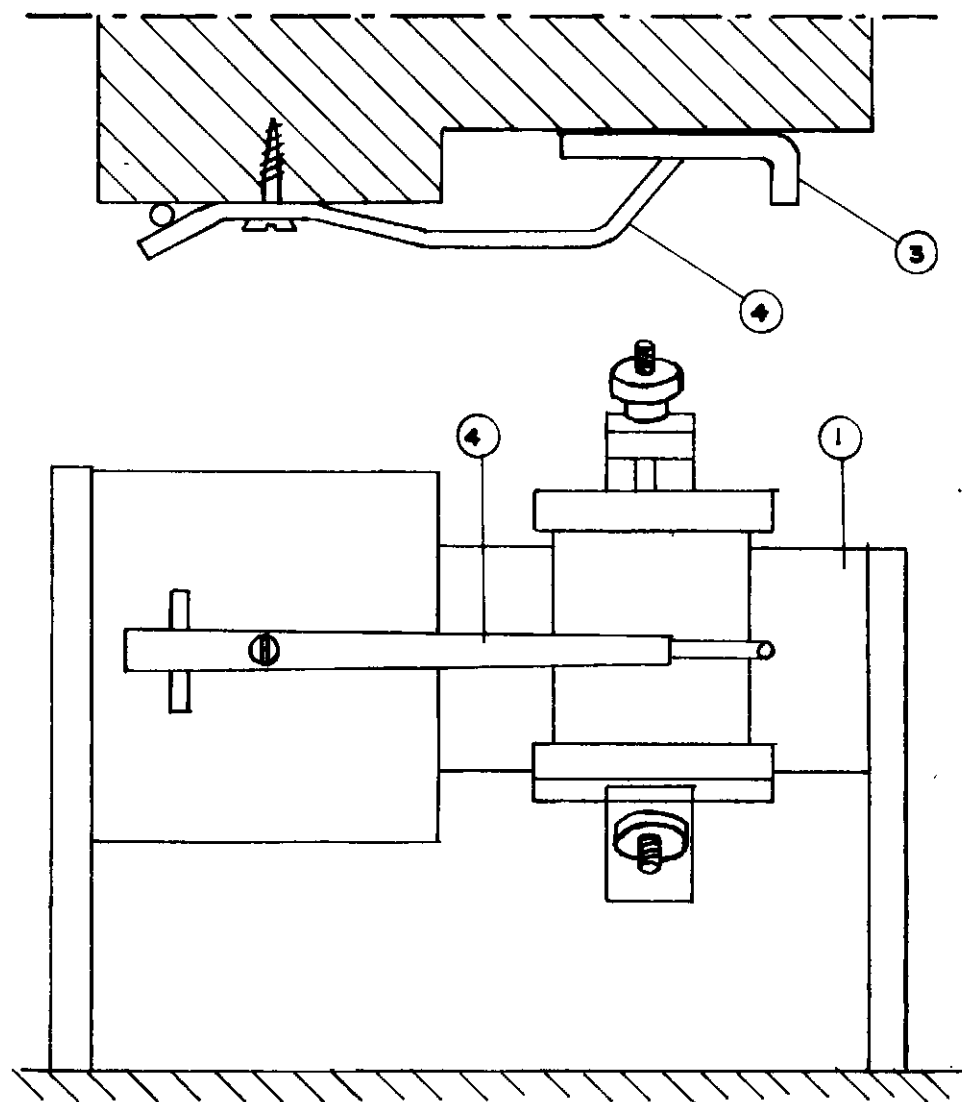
SOLDAGEM DOS TUBOS
